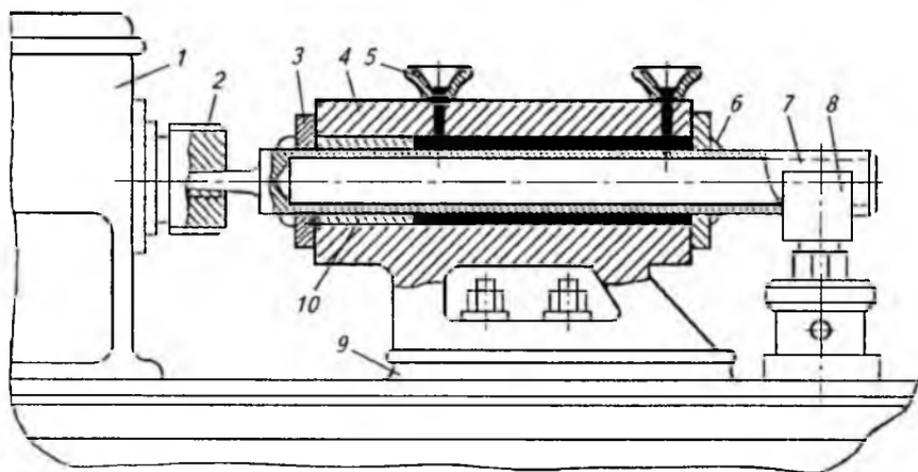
Схема восстановления отверстия под пиноль в корпусе задней бабки:
